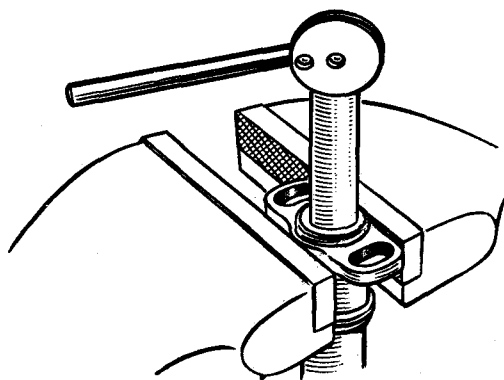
Установка приспособления для извлечения нагнетательного клапана
